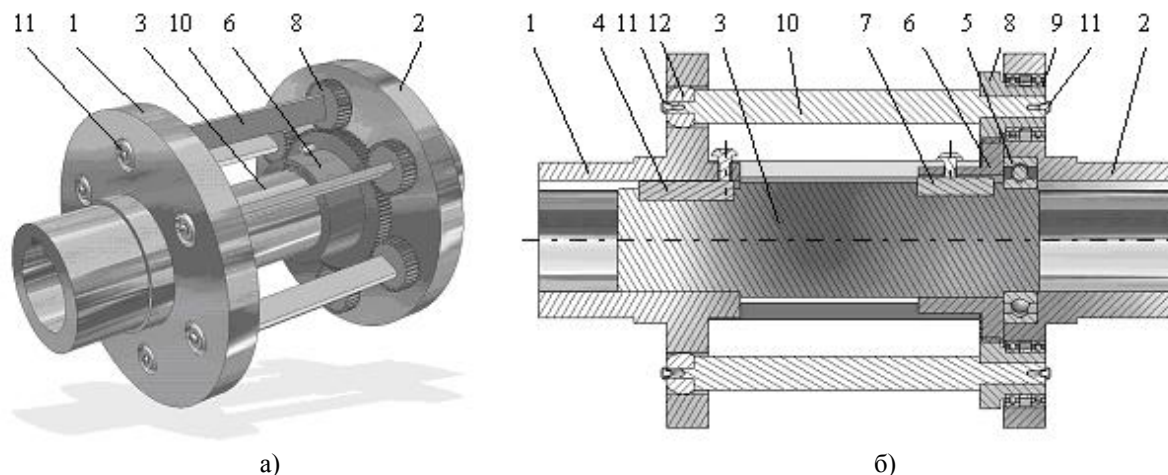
Віброізолюючий пристрій з механічним зворотнім зв'язком: а) конструктивне виконання; б) головний перетин конструкції.
